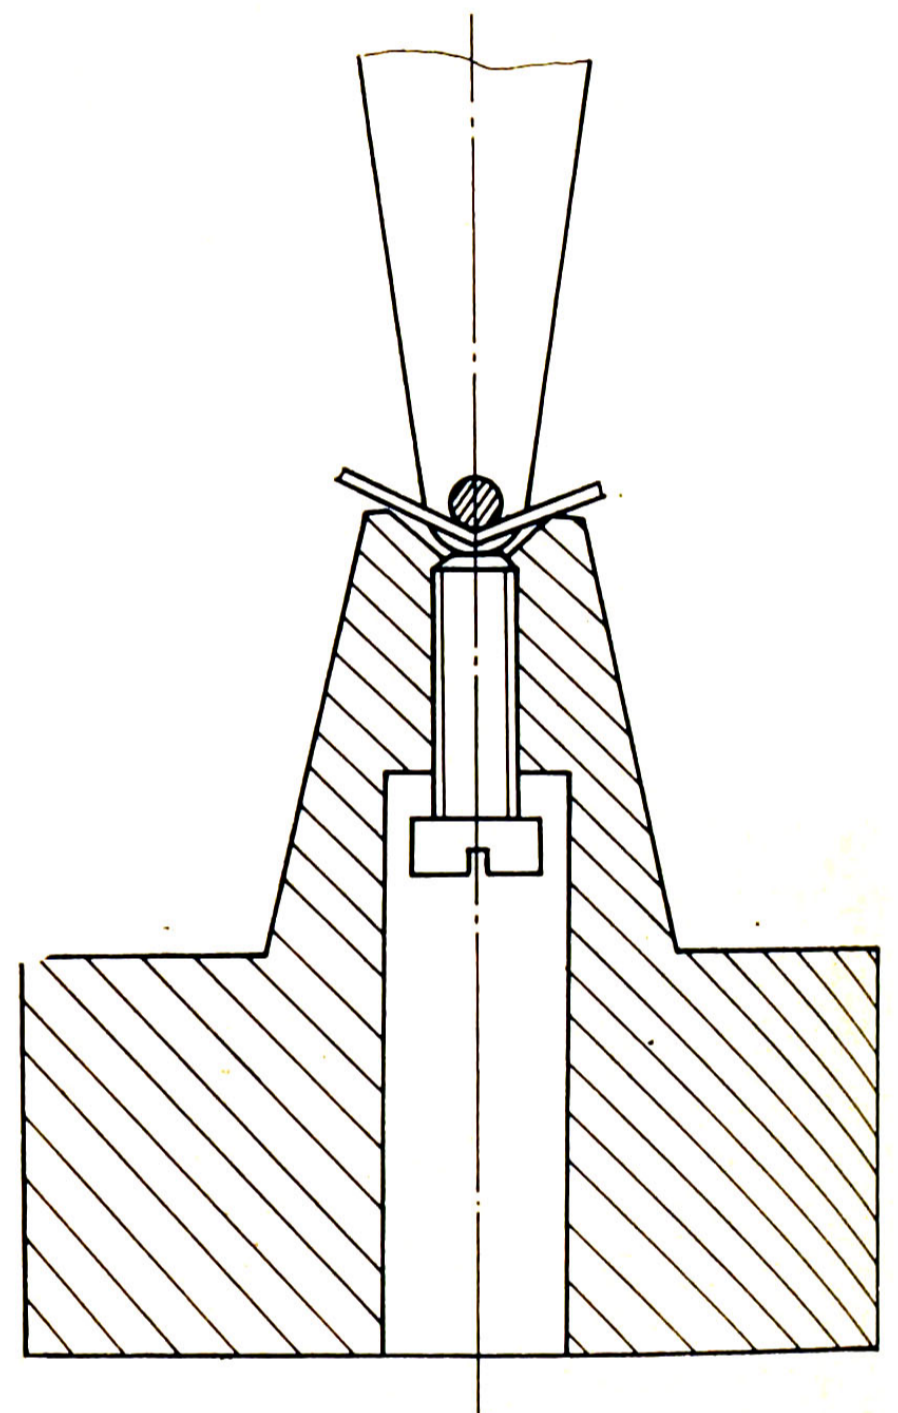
Spiralzange mit eingesetztem Stift und Amboß mit Anschlag zum Biegen des Knies der Breguet-Spirale
